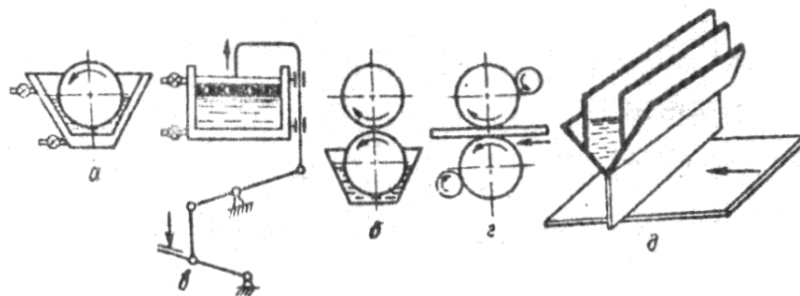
Схеми пристроїв для нанесення клею: а - одновальцьовий;
